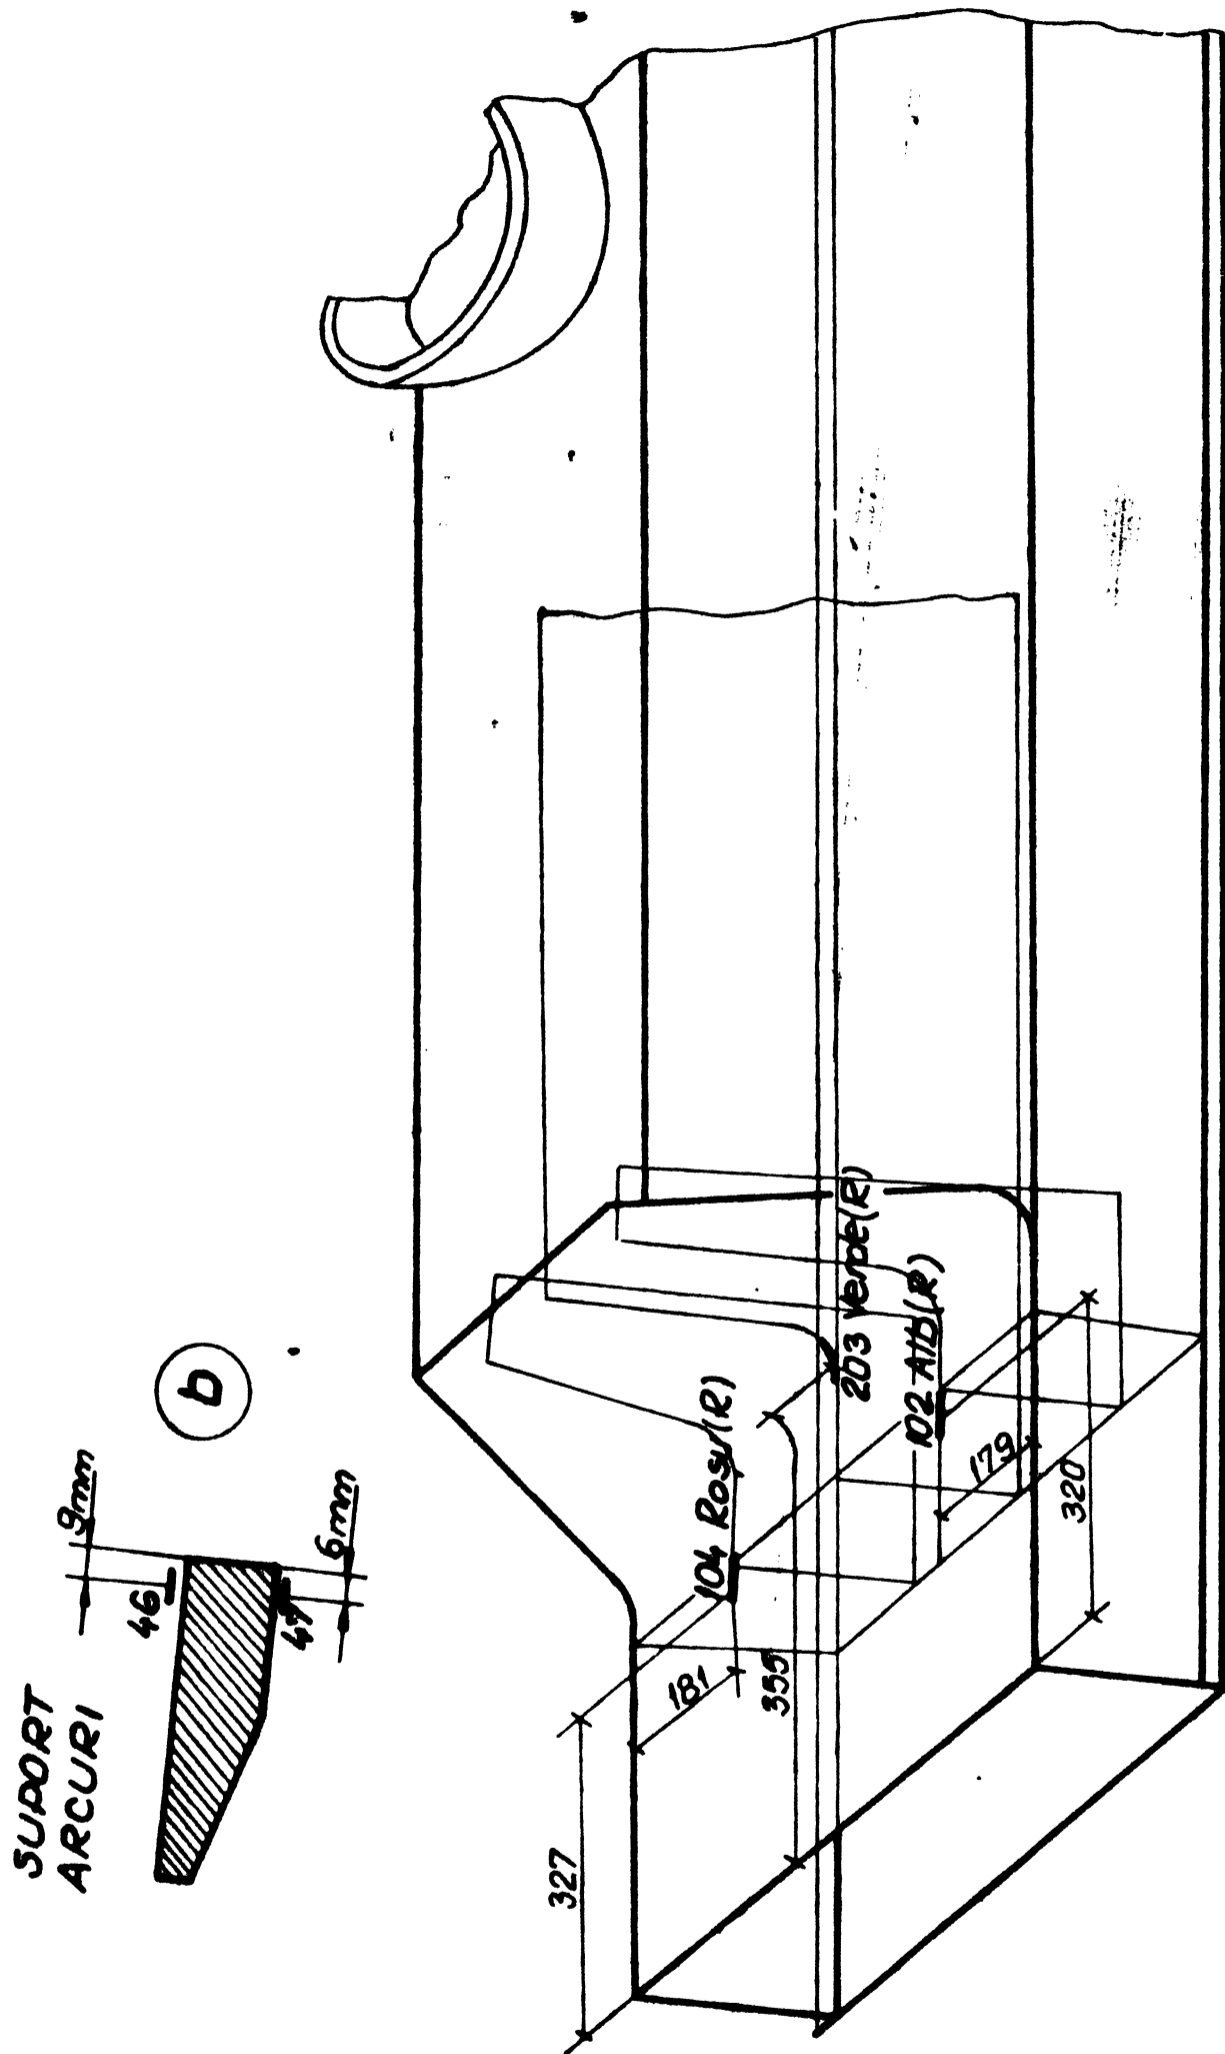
Planul de amplasare TER pe traversa crapodinei.
